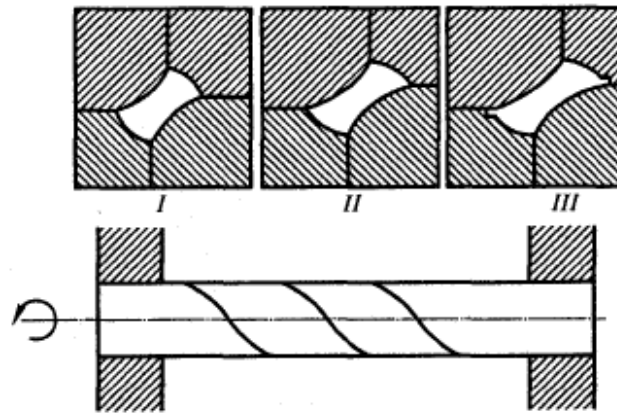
Гаряче вальцювання заготовок з послідуною завивкою гвинтових канавок: I, II і III – відповідно перший, другий і третій струмки для прокатки профіля свердла
